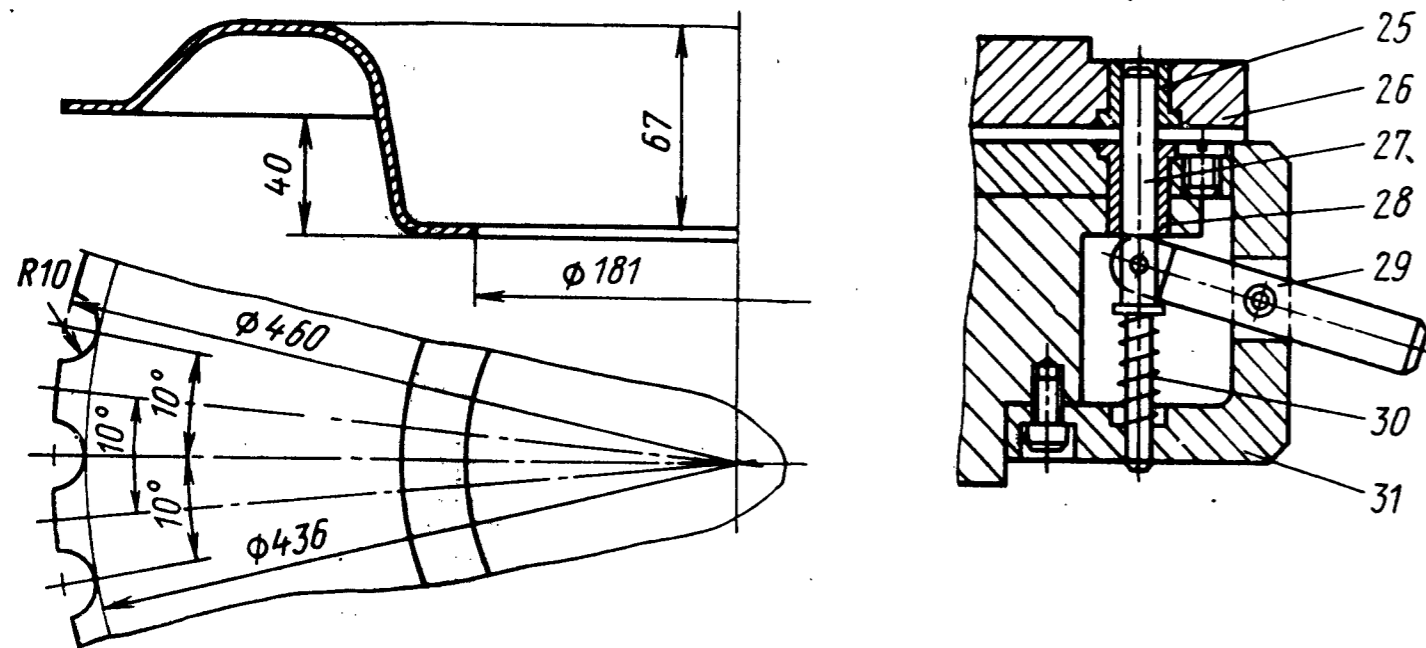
Штамп двухпуансонный делительный для пробивки отверстий в экране
